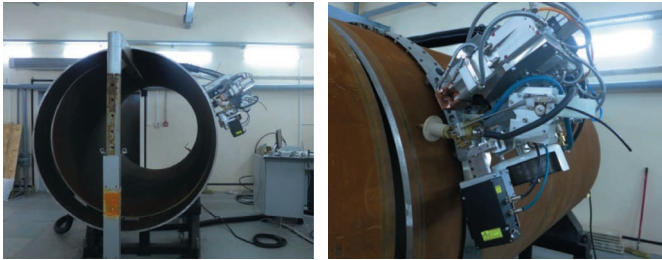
Мобильный комплекс для орбитальной лазерно-дуговой сварки.
